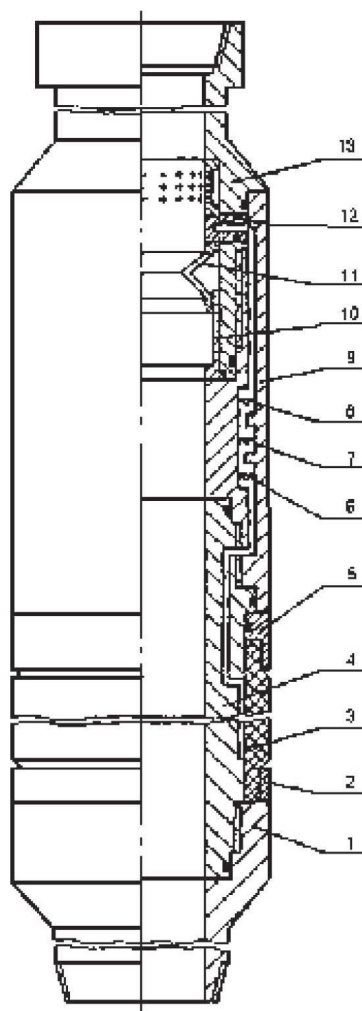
Пакер проходной гидравлический универсальный заколонный типа ППГУ:
